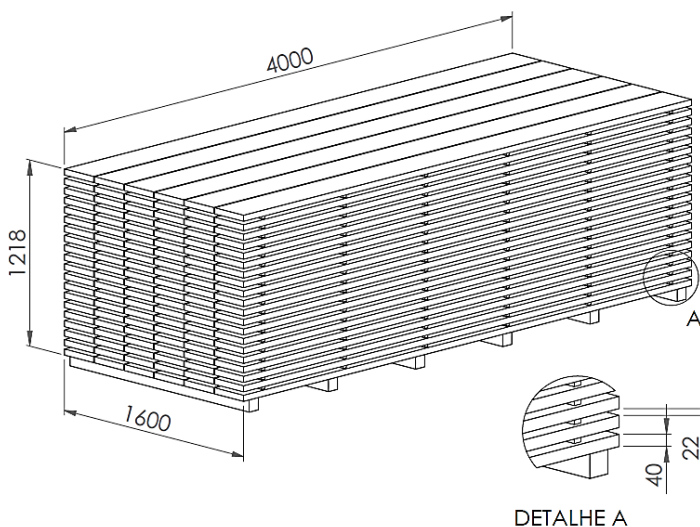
Pilha unitária de madeira (dimensões em mm)
